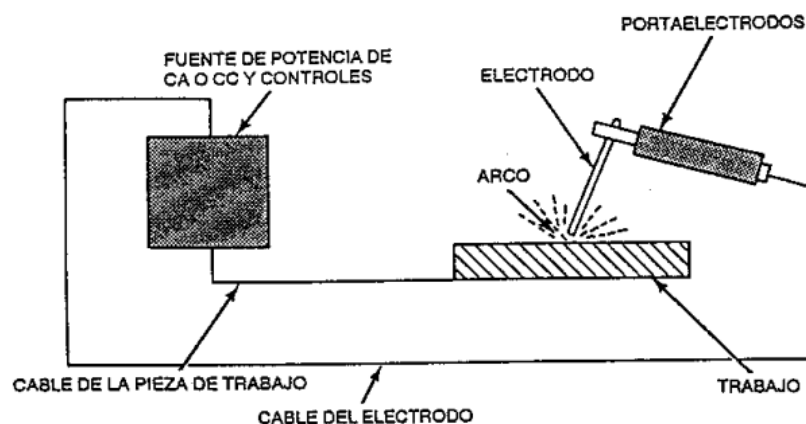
Elementos de un circuito de soldadura típico en la soldadura por arco de metal
